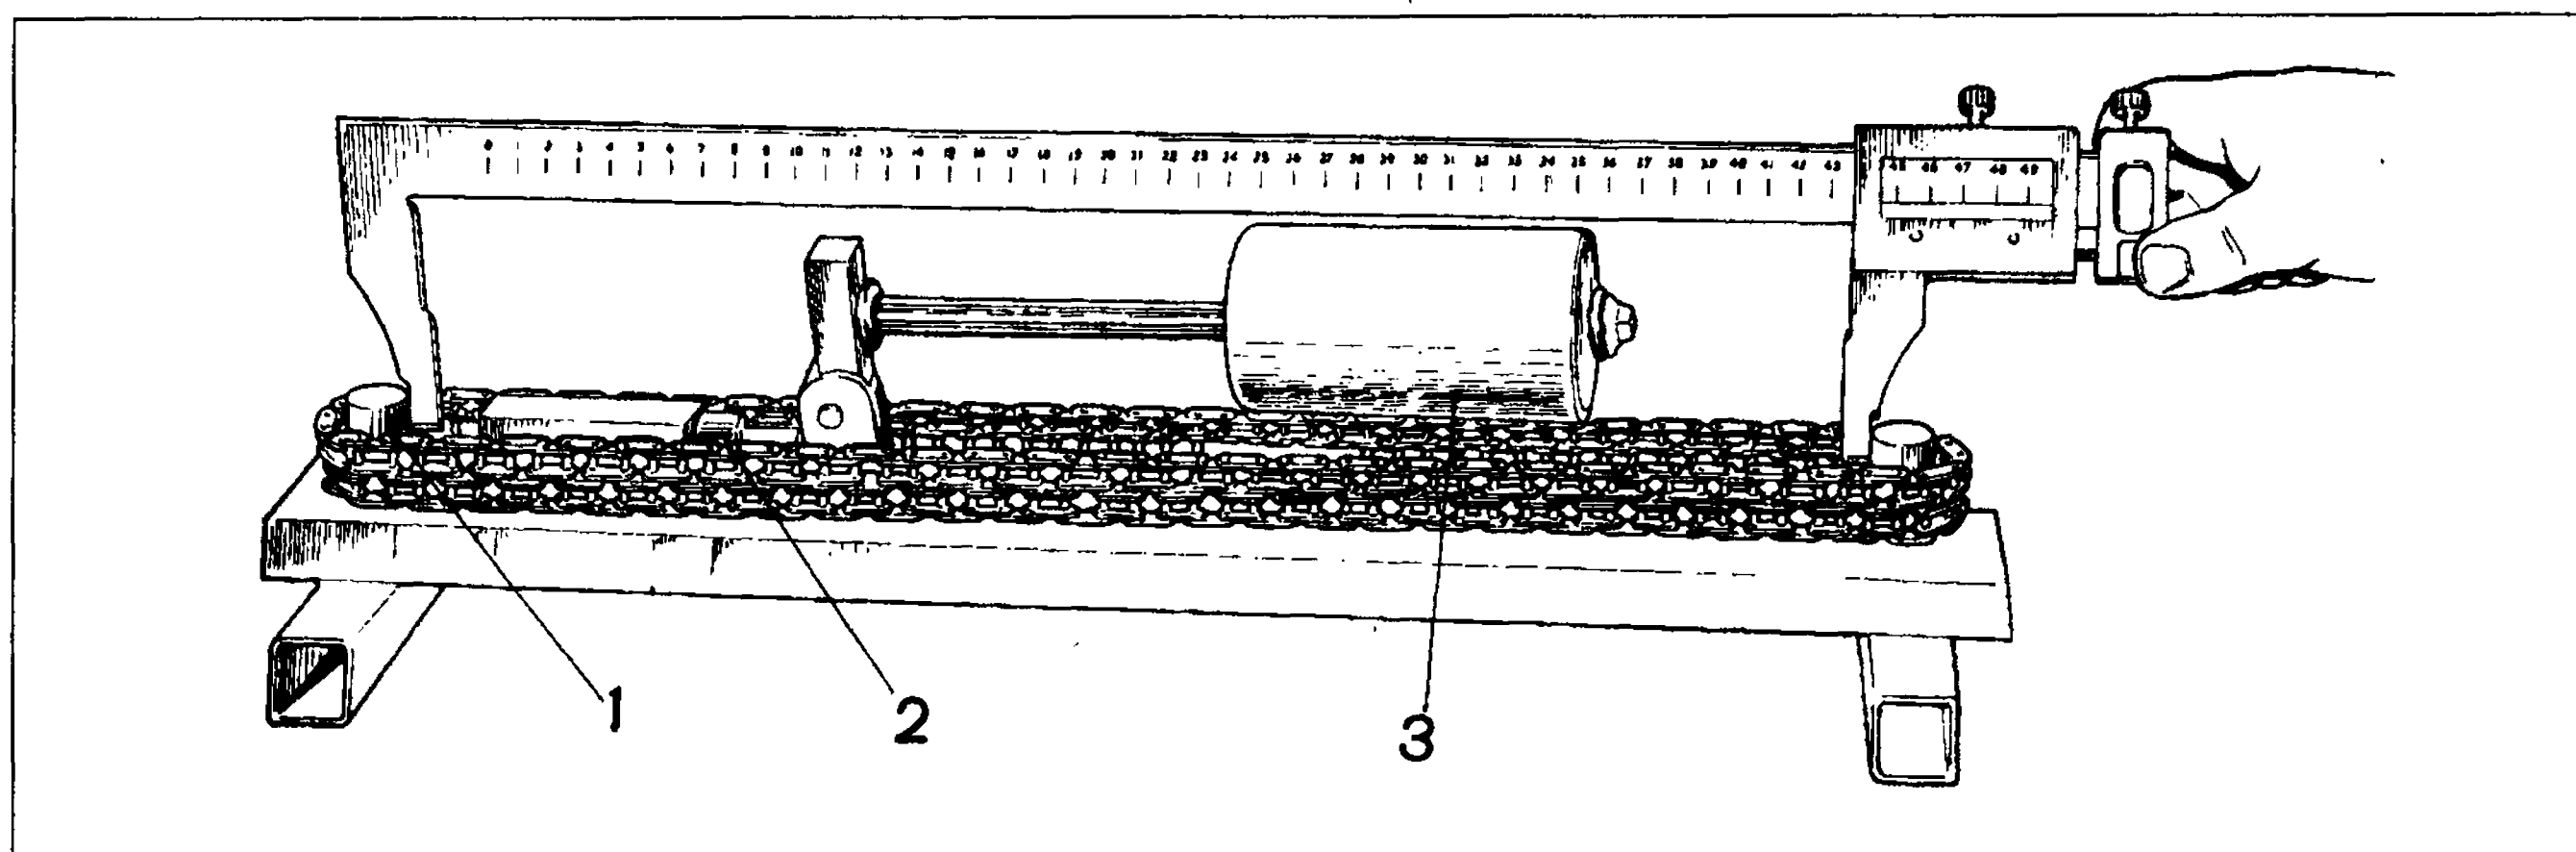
Приспособление 67.7824.9521 для проверки износа (вытяжки) цепи:
